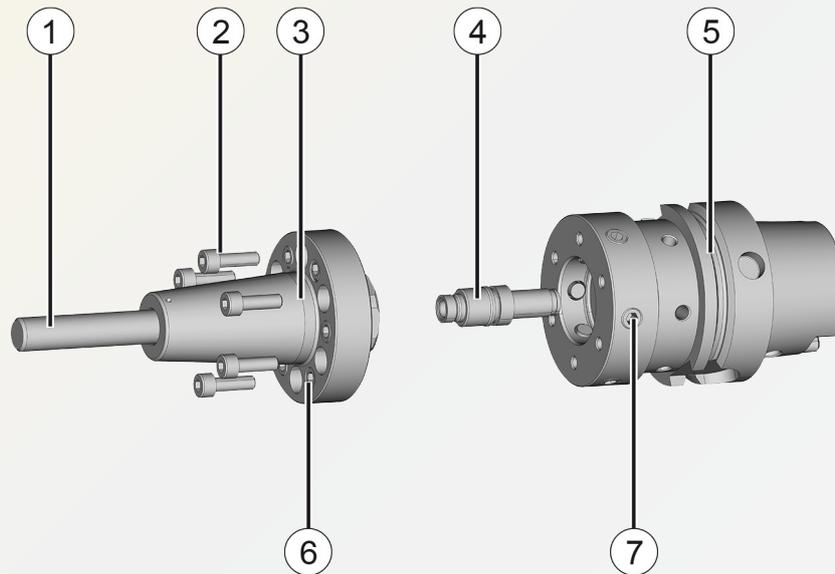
vue éclatée du module 6x6 adaptateur de positionnement
